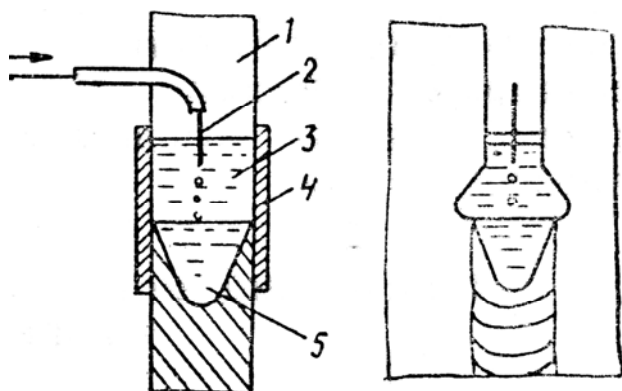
Принципиальная схема электрошлаковой сварки
